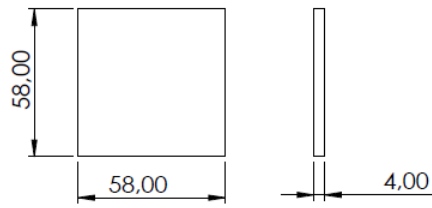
7 Diseño de la probeta a Impacto (Dimensiones en mm)
